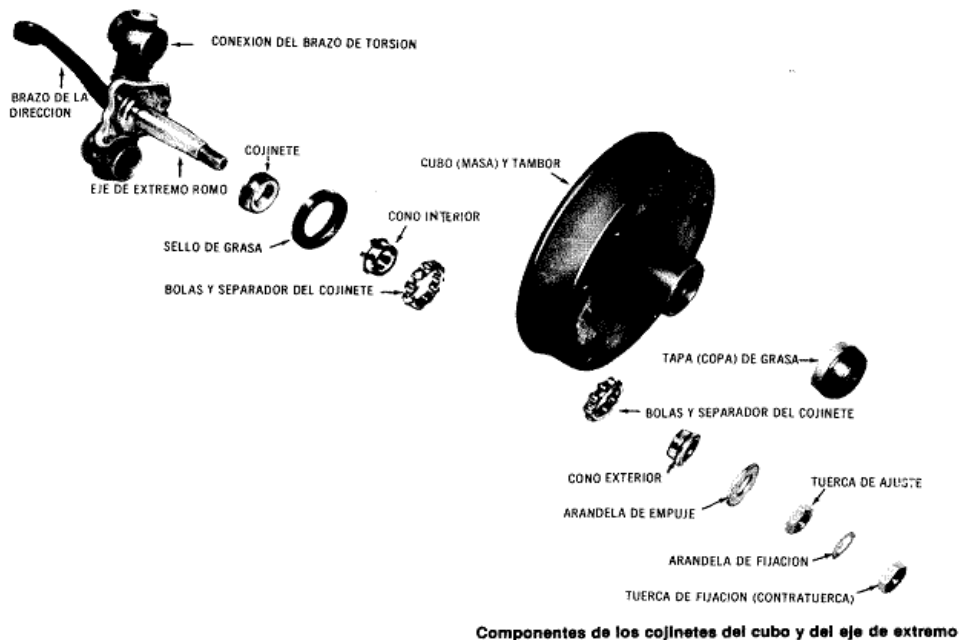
Componentes y orden de ensamblado del cojinete y extremo romo.
